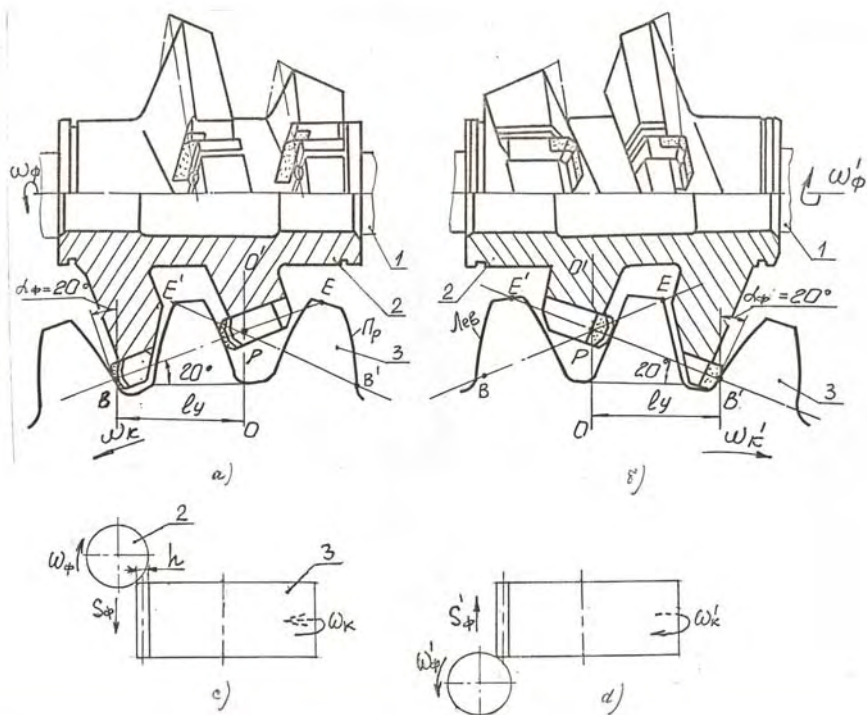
Схема обработки зубьев колеса одним правым корпусом фрезы
